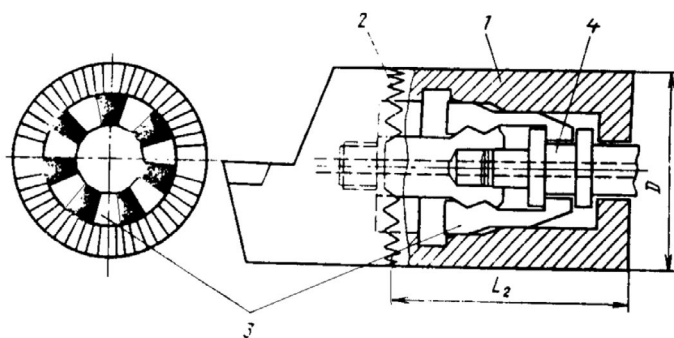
Крепление головки токарного резца с помощью муфты Хирта [9]:
